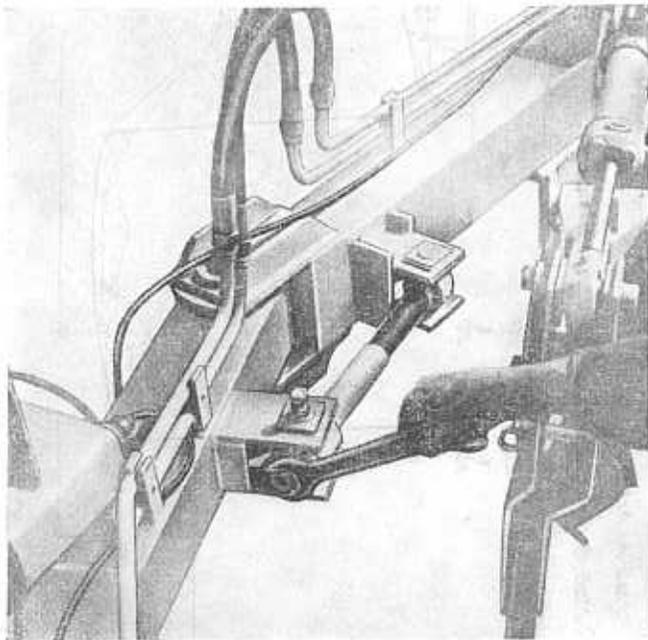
Spindel zum Schwenken des Hinterradauslegers
